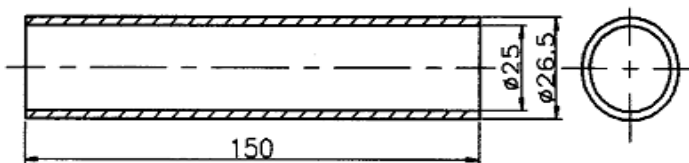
Эскиз обрабатываемой трубы из стали STS304
